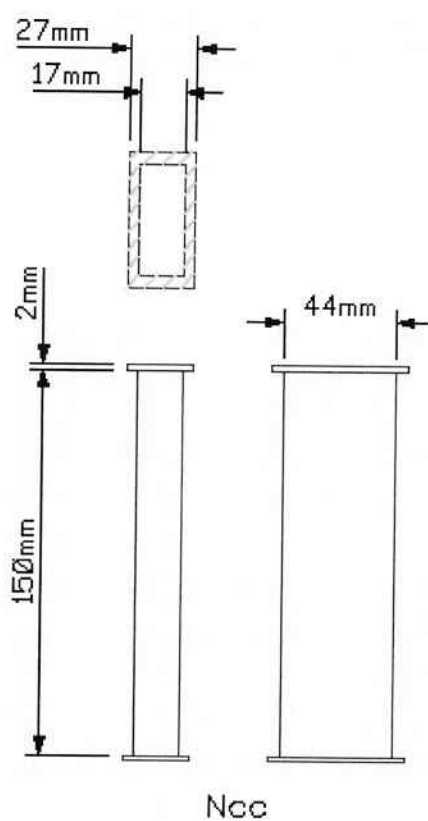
Vistas e dimensões do molde para as bobinas DC
